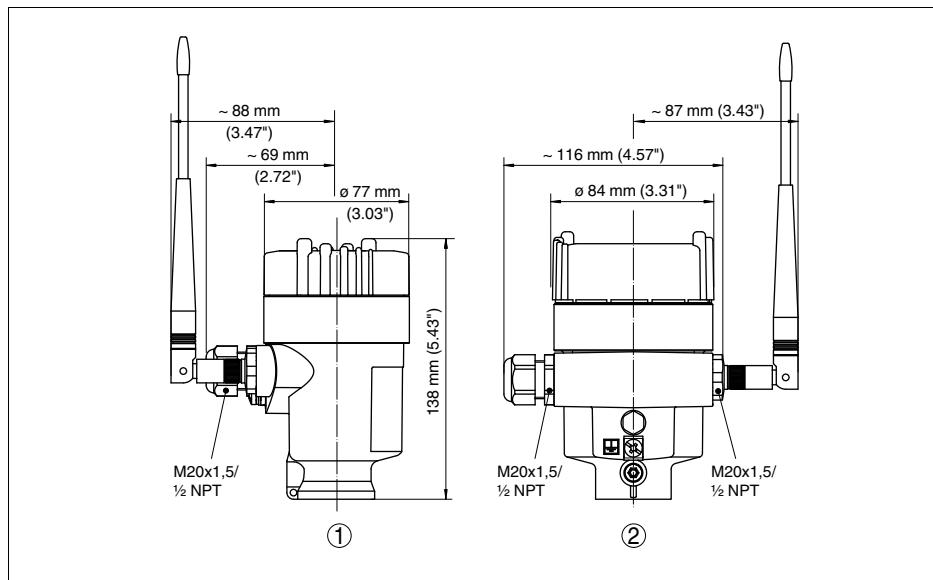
Корпус с электроникой: с установленным модулем PLICSCOM пластиковый корпус выше на 11 мм (0.43 in), а алюминиевый - на 9 мм (0.35 in)
